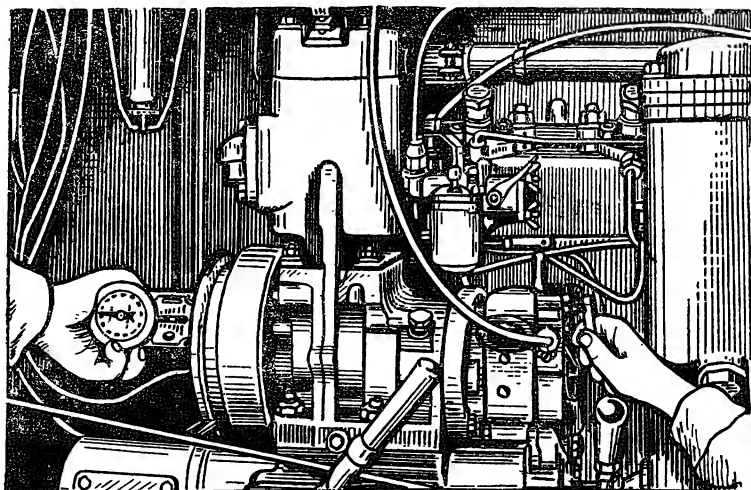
Регулировка натяжения пружины регулятора пускового двигателя
